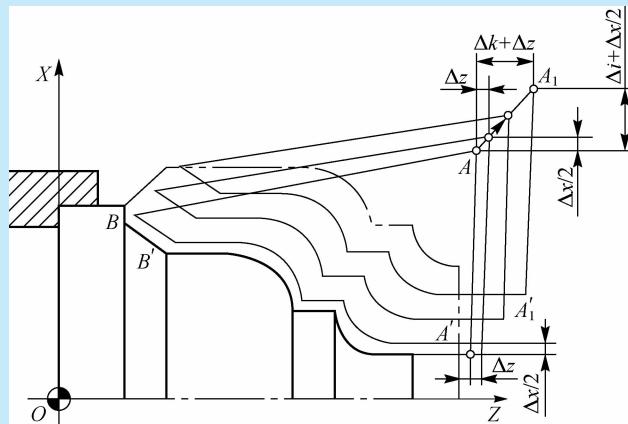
封闭轮廓车削复合循环指令 G73 加工轨迹
